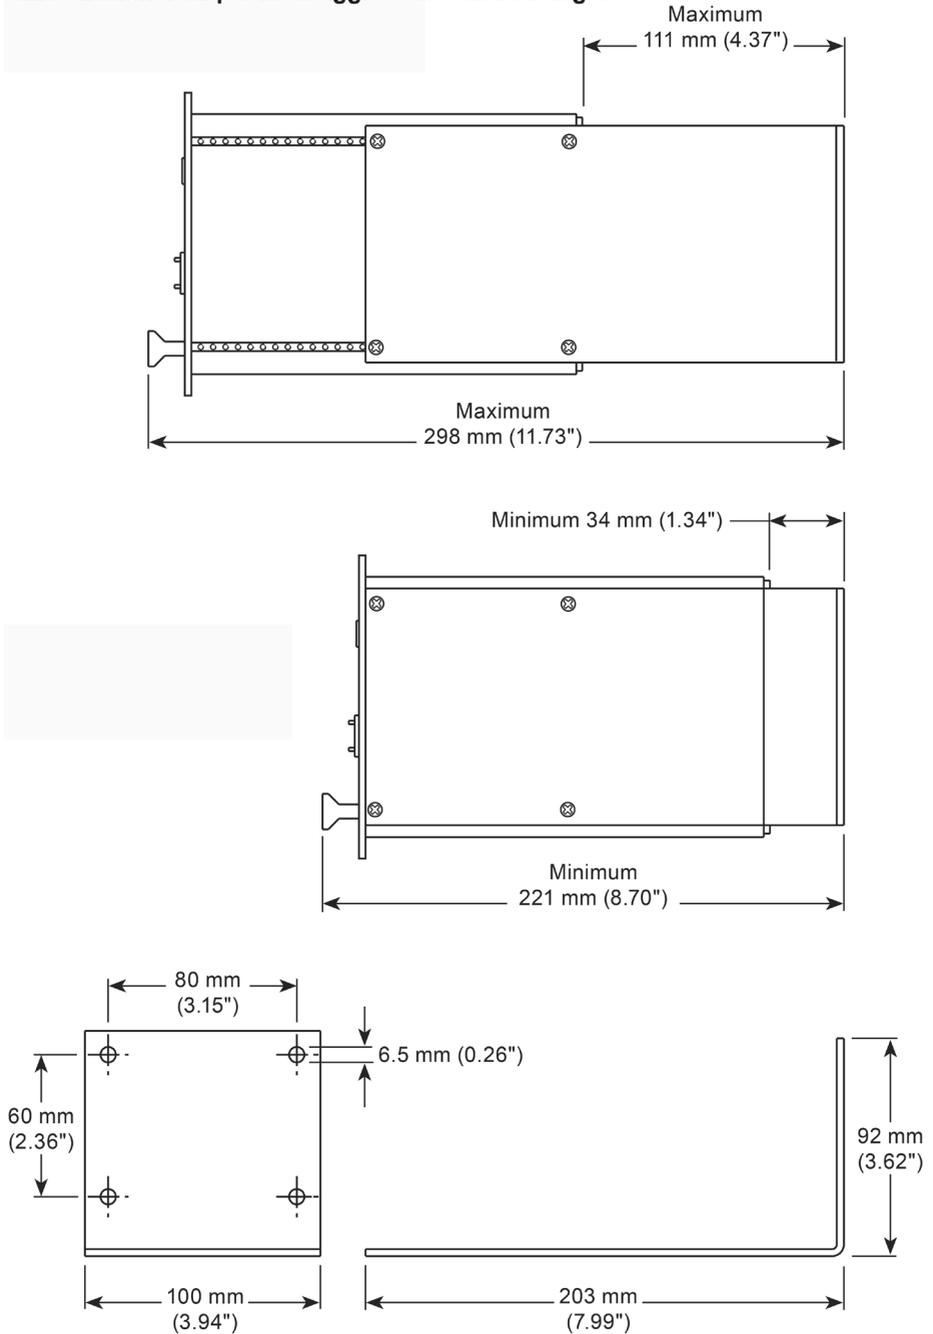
Dimensioni per montaggio con staffa ad angolo W19
